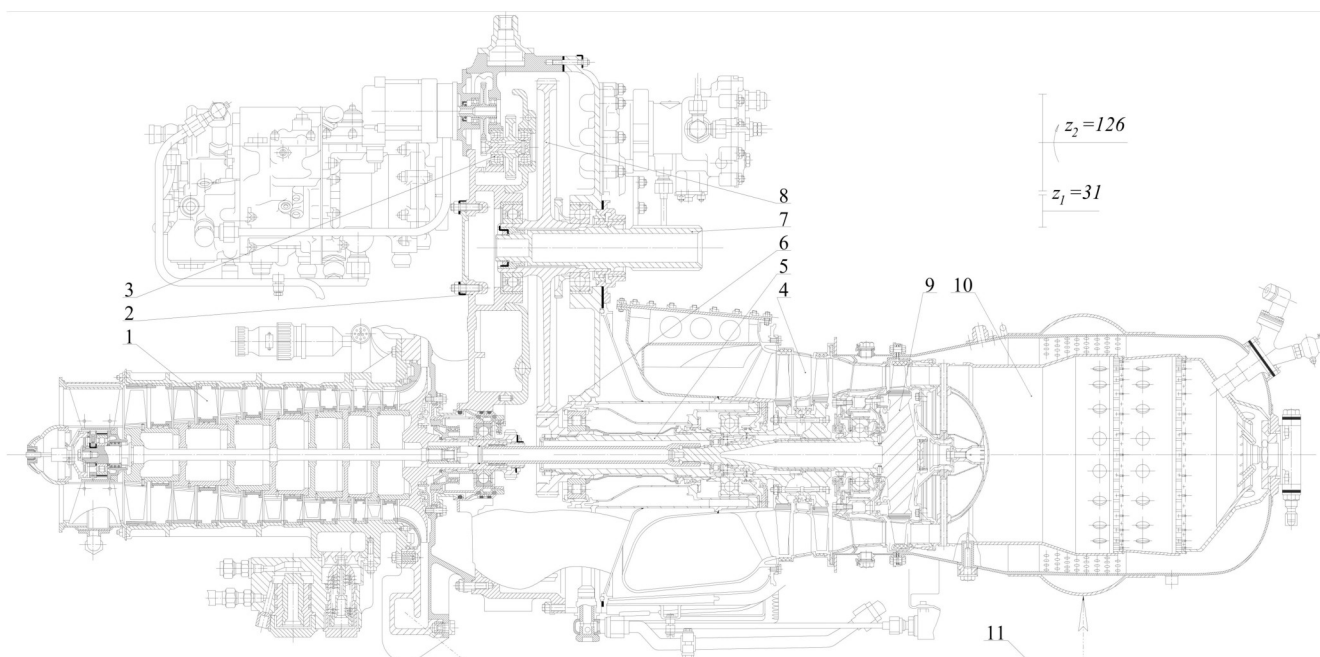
Редуктор ТВад ГТД - 350, размещенный в середине двигателя:
